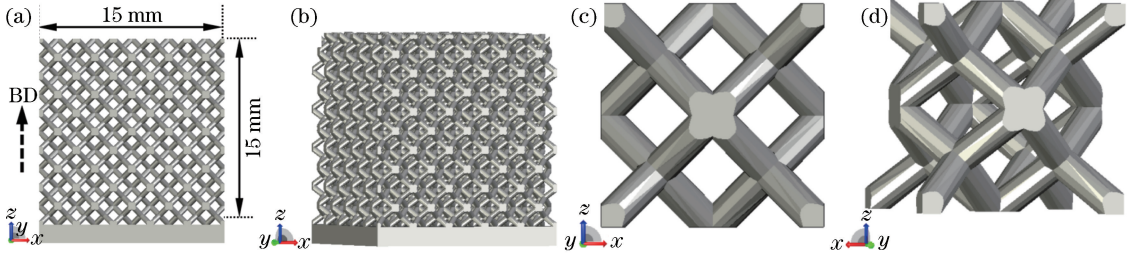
点阵结构示意图。(a) 点阵结构主视图; (b) 点阵结构斜视图; (c) 单元晶胞主视图; (d) 单元晶胞斜视图
